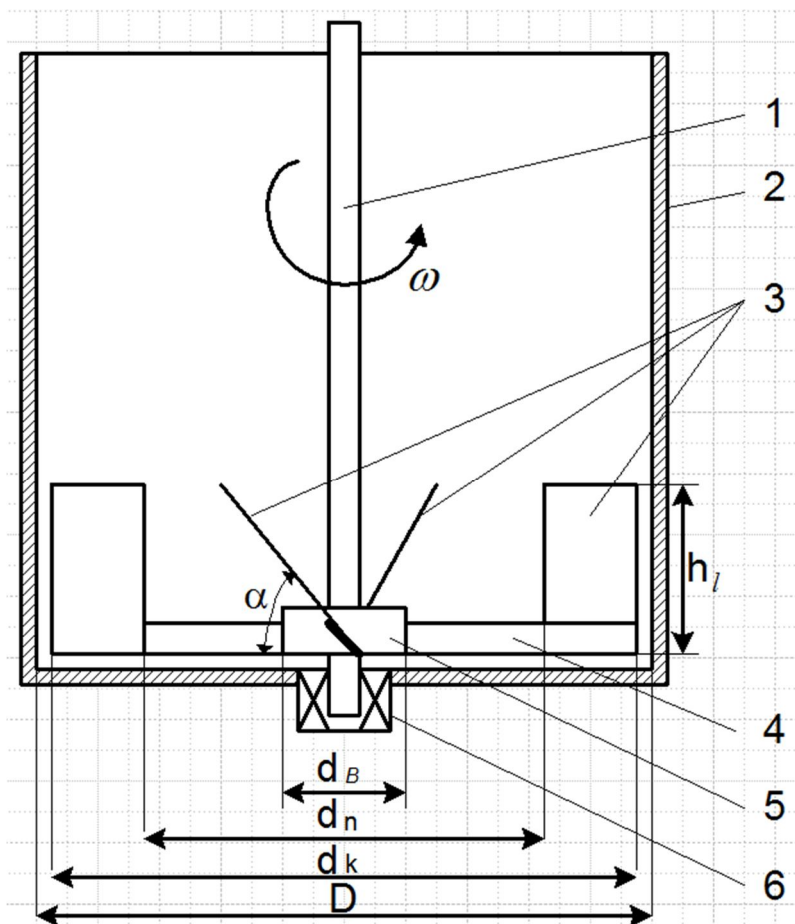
Схема смесителя: 1 – вал; 2 – емкость смесителя; 3 – лопатки; 4 — лопасть; 5 – мешалка; 6 – подшипниковая опора
